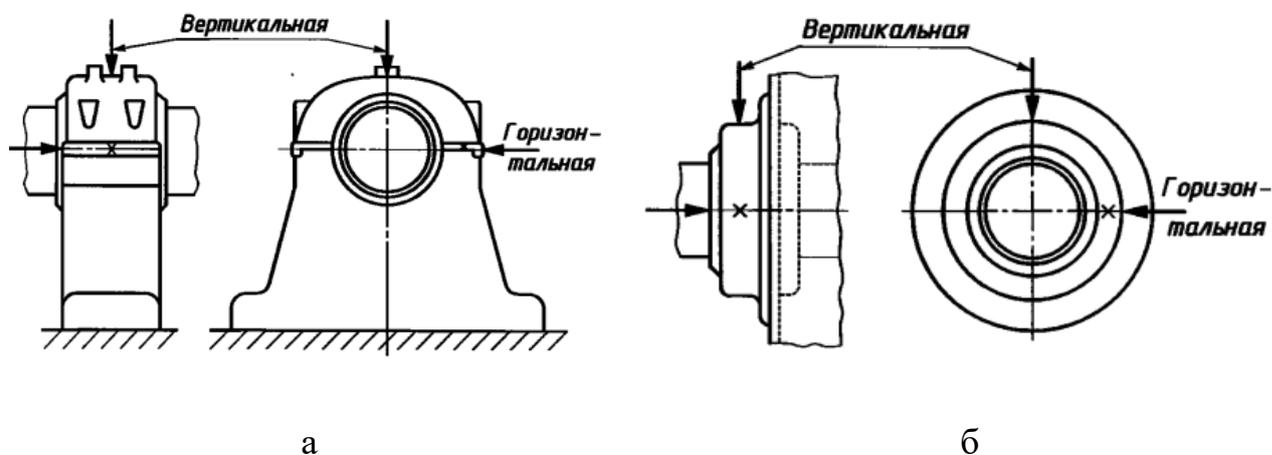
а – точки измерения на опоре подшипника; б – точки измерения на корпусе подшипника
